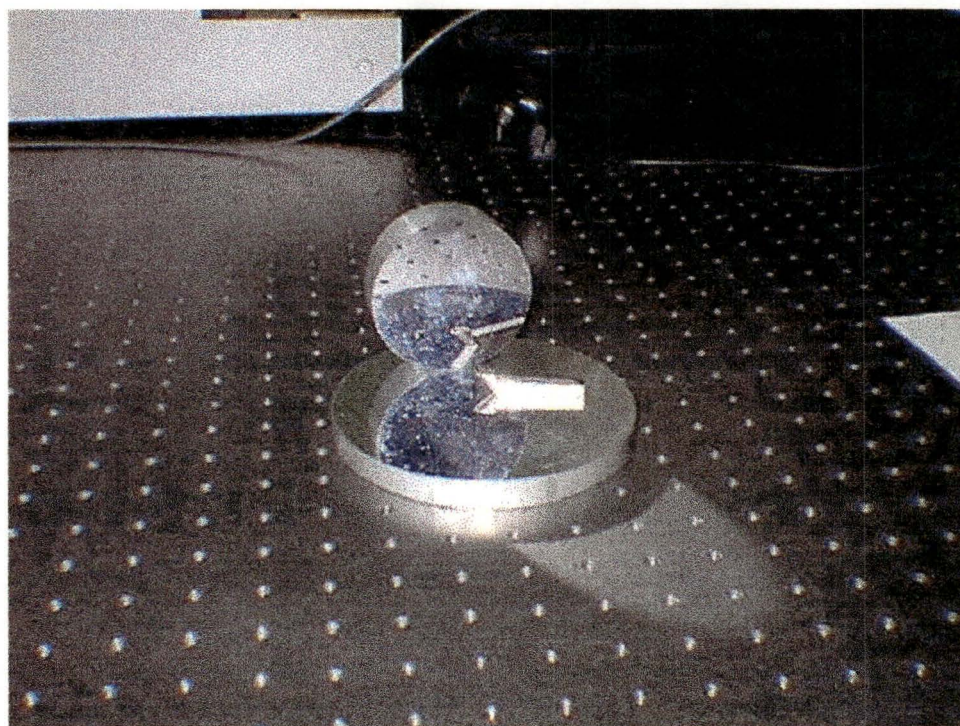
Ferramenta com ponta de diamante e duas superfícies usinadas
